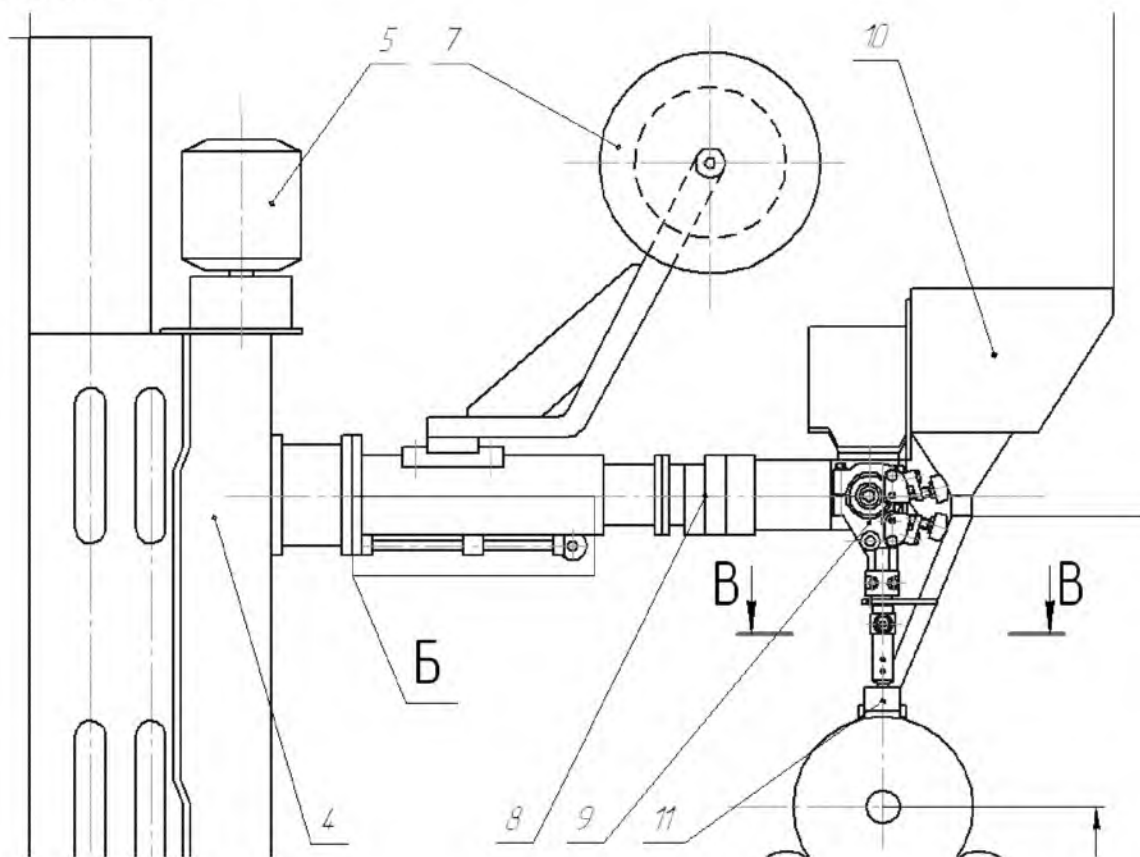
Установка для сварки кольцевых швов
